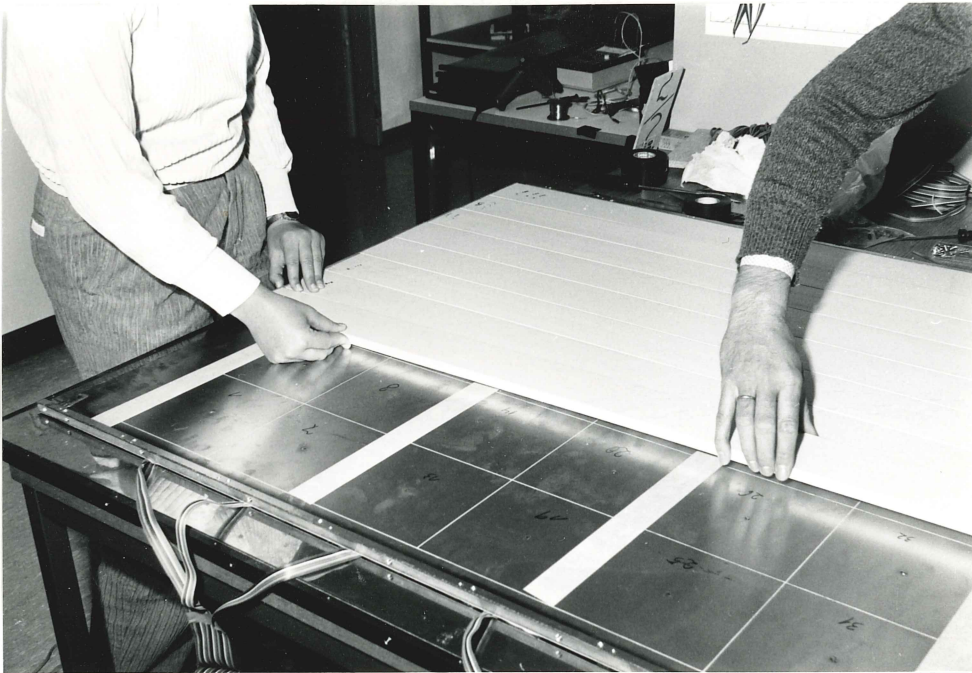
Aufkleben der Tubes auf die Padplatte
